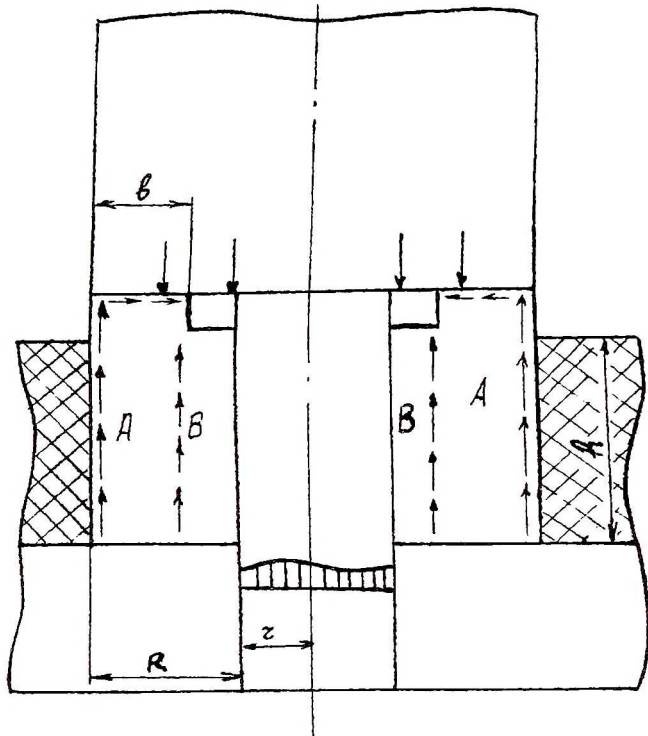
Схема деформирования подкрепляющей втулки и листовой заготовки
